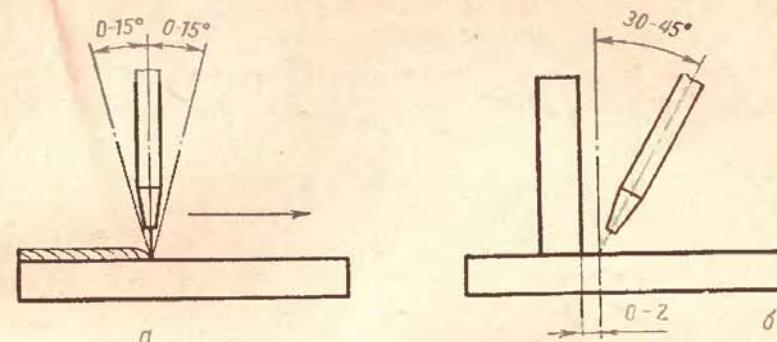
Направление электрода при полуавтоматической сварке порошковой проволокой соединений:
